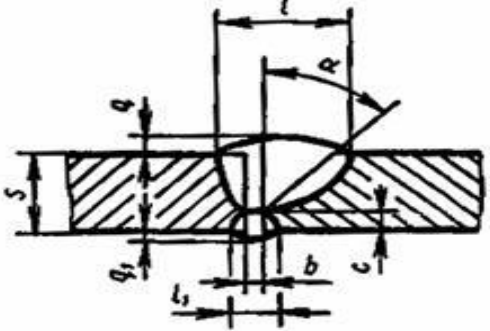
Расчетная схема сварки опорной лапы.
